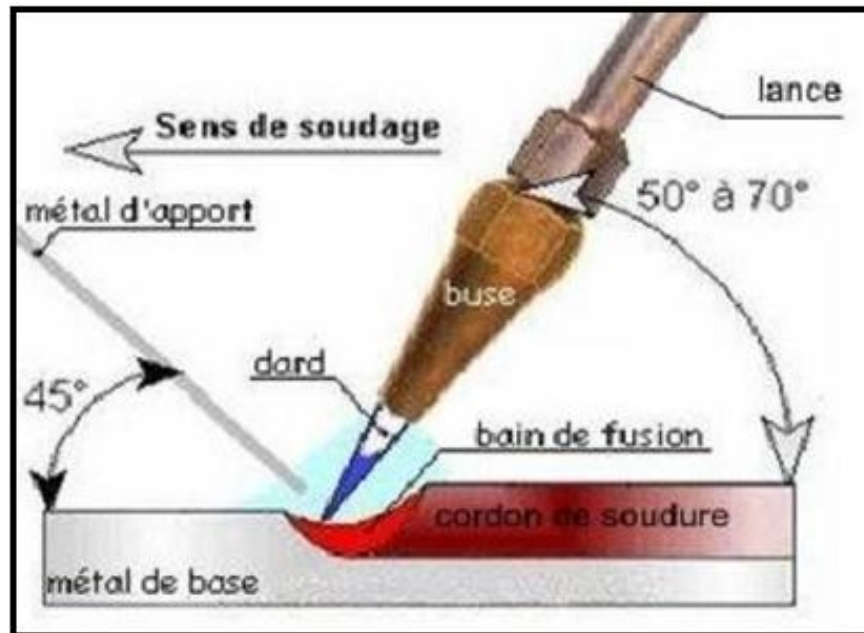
Illustration du procédé de soudage à la flamme oxyacétylénique [8].
